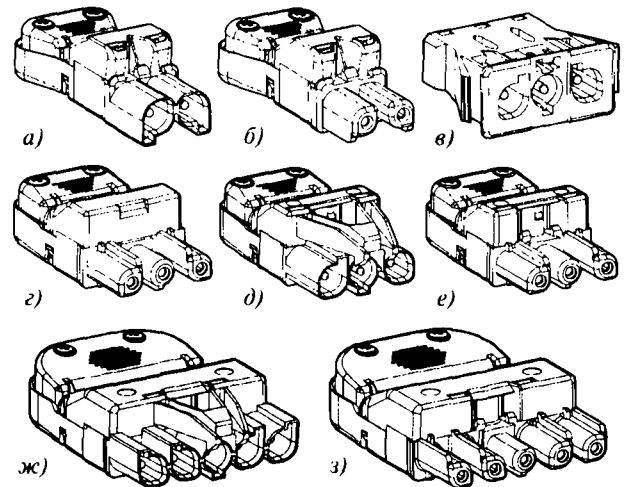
Штепсельные соединители с защитными крышками: а, б — двухполюсные без заземления; в, г, д, е — двухполюсные с контактами для заземления; ж, з — четырехполюсные с контактами для заземления; а, в, д, ж — вилки; б, г, е, з — розетки
